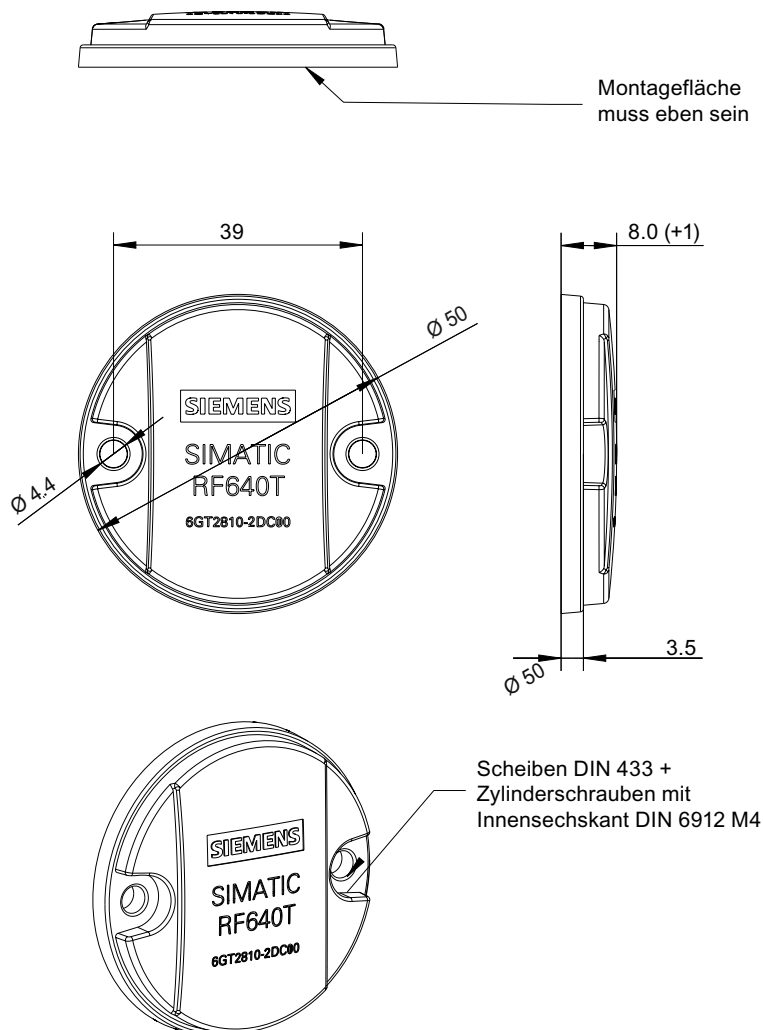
SIMATIC RF640T Gen 2 UHF Tool Tag Version 1
